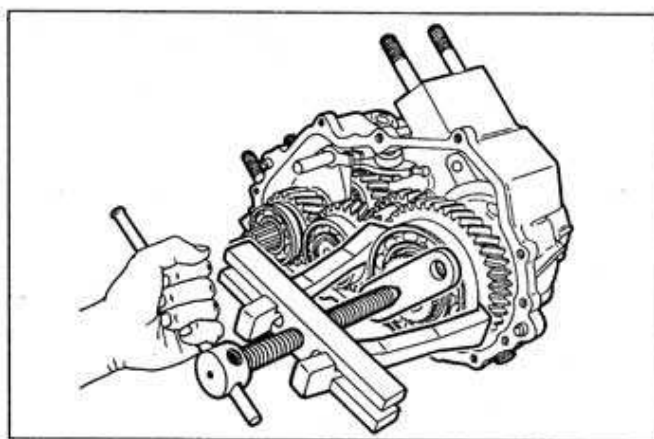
Спрессовка подшипника с шестерни дифференциала
